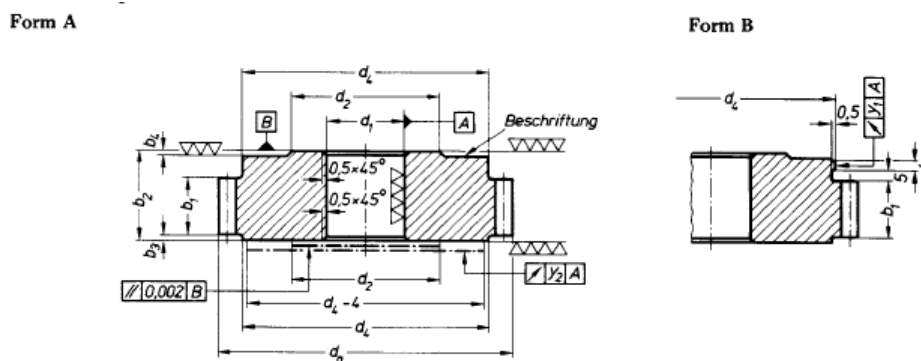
Engranaje patrón desde m 0,5 hasta 3,55mm (fuente [13])
